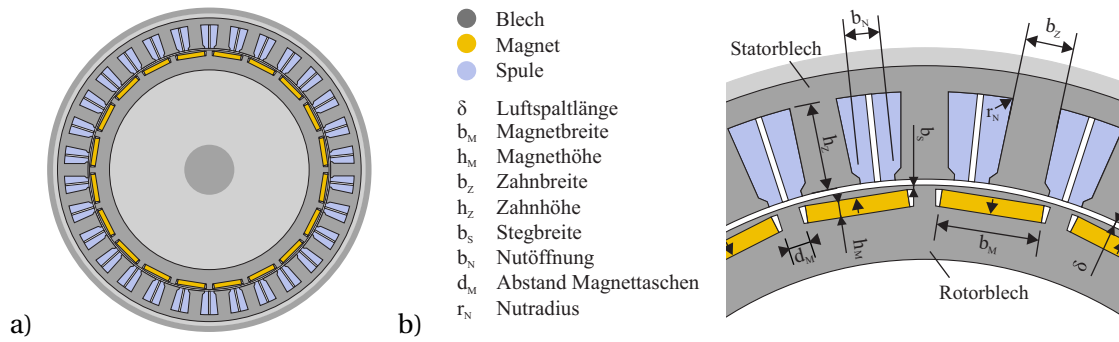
Querschnitt einer IPMSM. a) Schnittansicht des kompletten Rotors. b) Detailansicht mit Bezeichnung der relevanten Größen für die Untersuchung produktionsbedingter Auswirkungen
